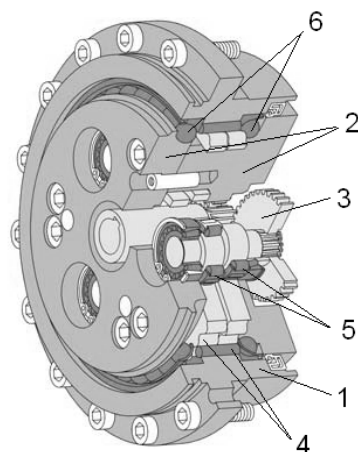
Планетарно-цевочный редуктор типа RV (схема 2К-V): 1 – корпус; 2 – водило; 3 – эвольвентный сателлит быстроходной ступени; 4 – эпициклоидный сателлит и цевка внецентроидного внутреннего цевочного зацепления; 5 – цилиндрические роликовые подшипники; 6 – шарики радиально-упорных совмещённых опор качения
